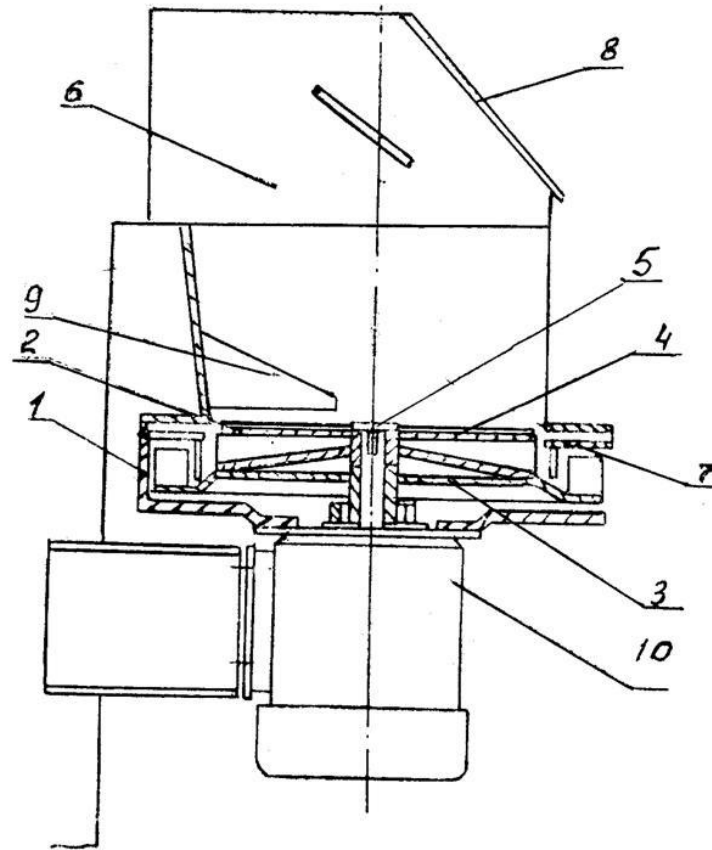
Подрібнювач: 1- корпус; 2- верхній диск; 3- нижній диск із лопатями; 4- ножі; 5- болт; 6- перехідник; 7- дека; 8- кришка; 9- протириз; 10-електродвигун.
